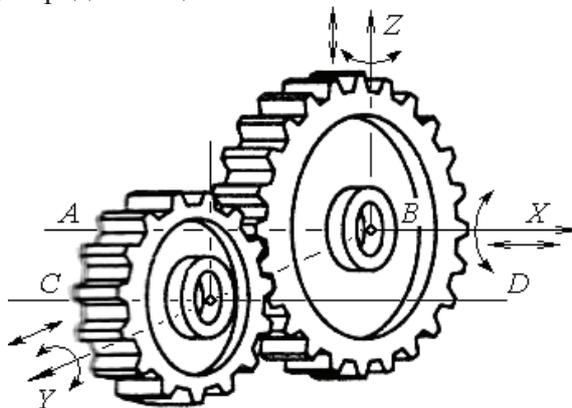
Схема цилиндрической зубчатой передачи в прямоугольной системе координат
